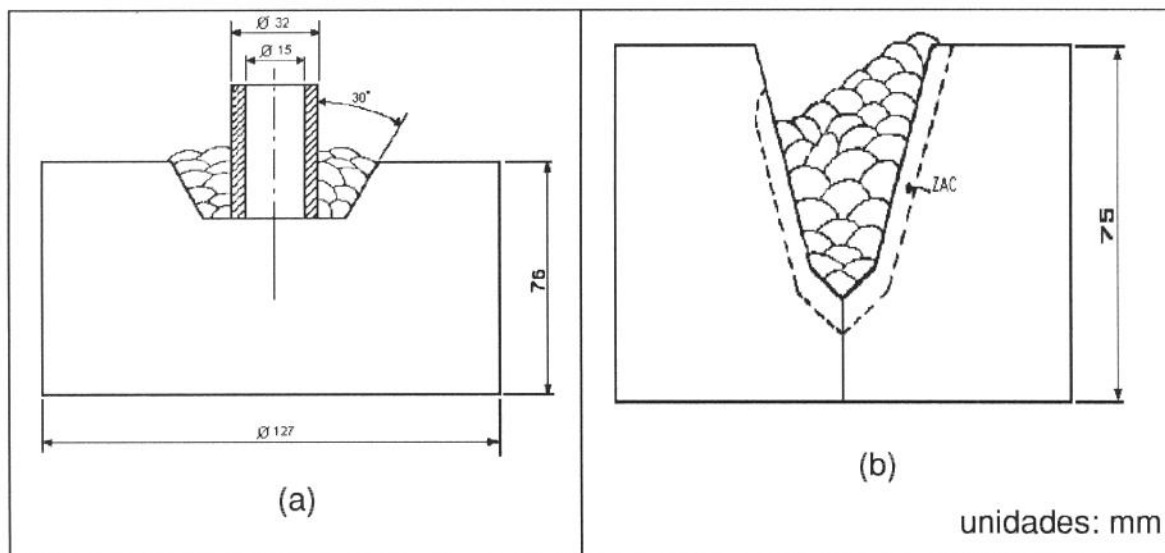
Testes de Glossop: (a) Teste de Glossop com tubo soldado, (b) Teste de Glossop com dois blocos soldados [5].
